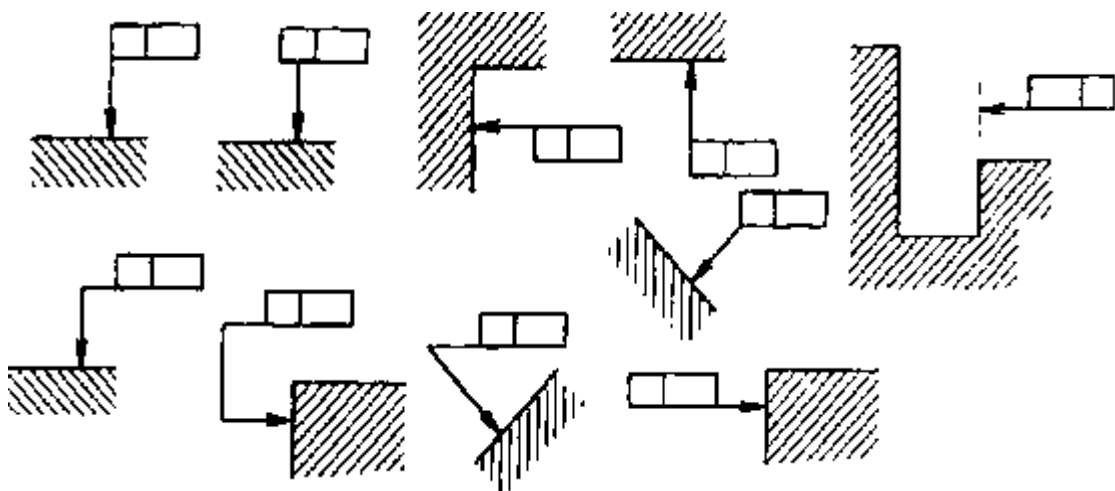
Приклади з'єднання рамок форми і розташування поверхонь з елементами деталі
